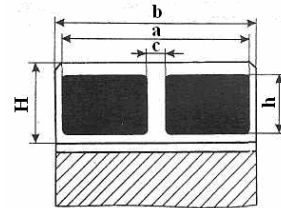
Контроль качества сборки прямозубчатого зацепления с помощью краски:
